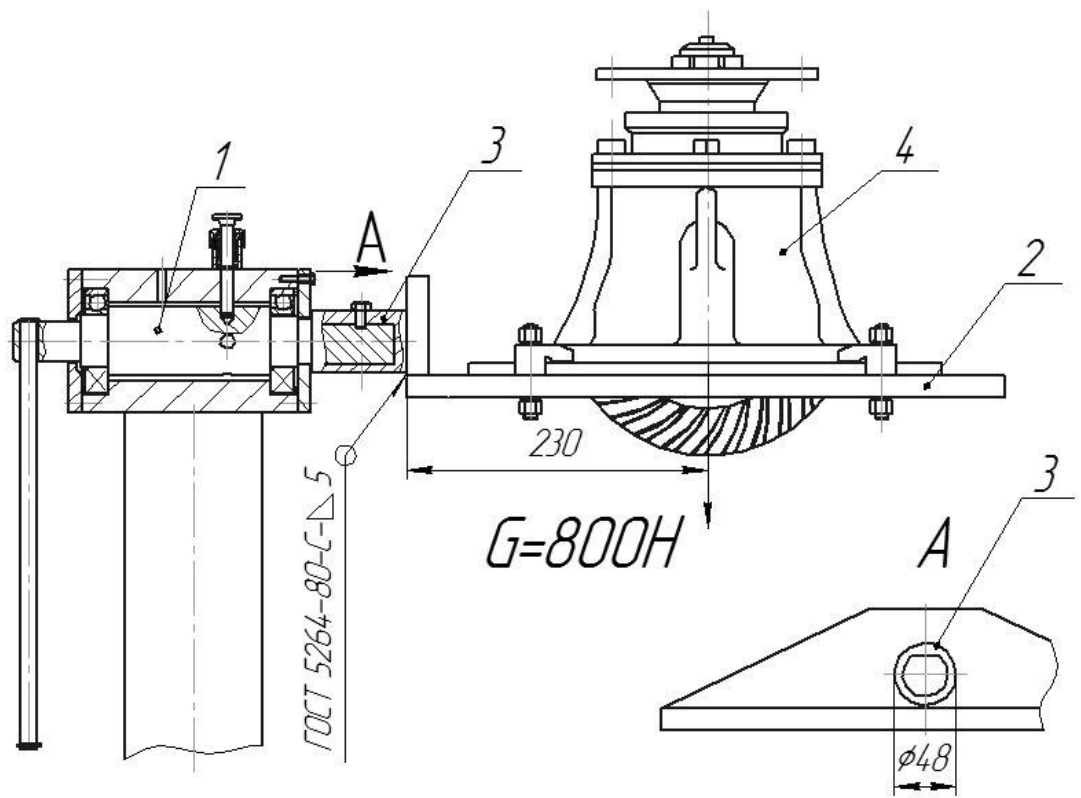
Расчетная схема сварного соединения втулки установочной плиты
